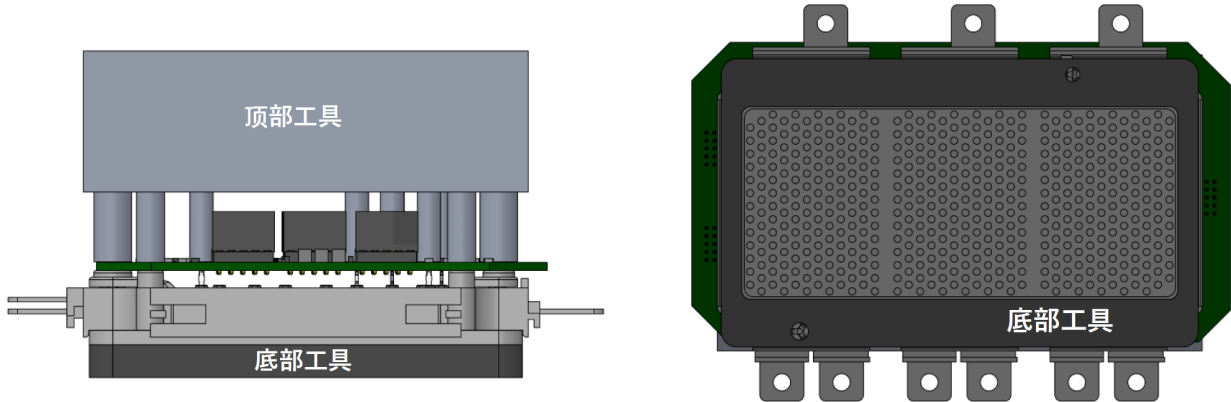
显示了适用于所有 Si-IGBT 版本模块的 PCB 装配工具
